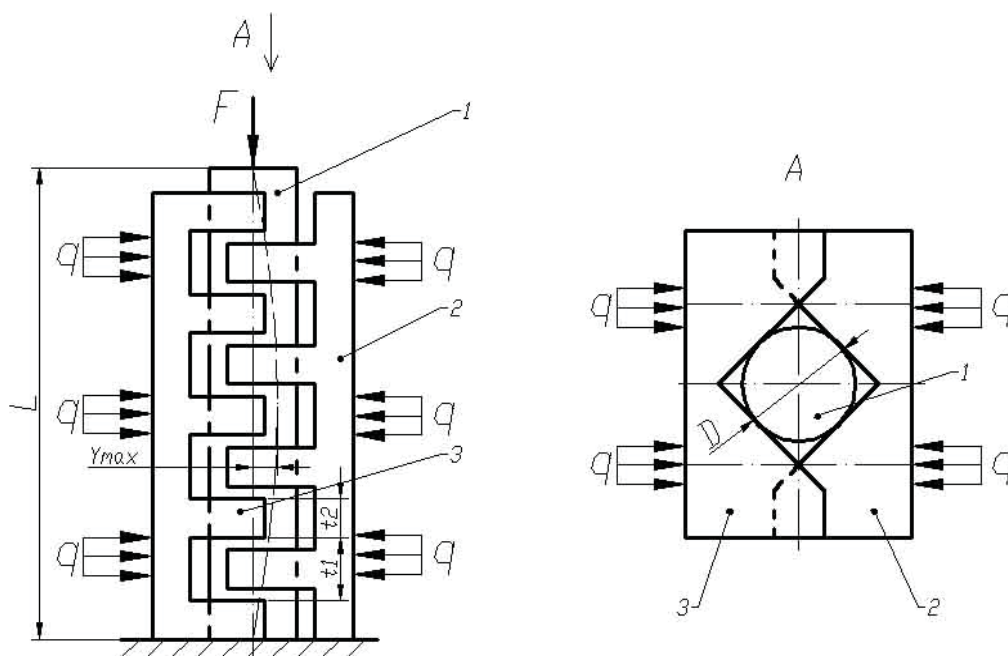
Схема правки мало жестких цилиндрических деталей стесненным сжатием: 1 - деталь; 2, 3 - призмы
